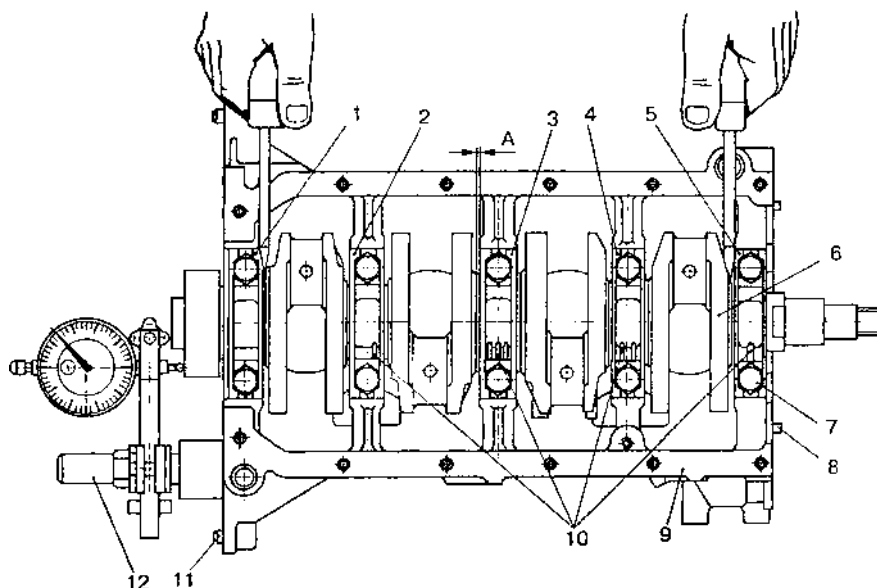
Проверка осевого разбега и маркировка крышек подшипников коленчатого вала:
